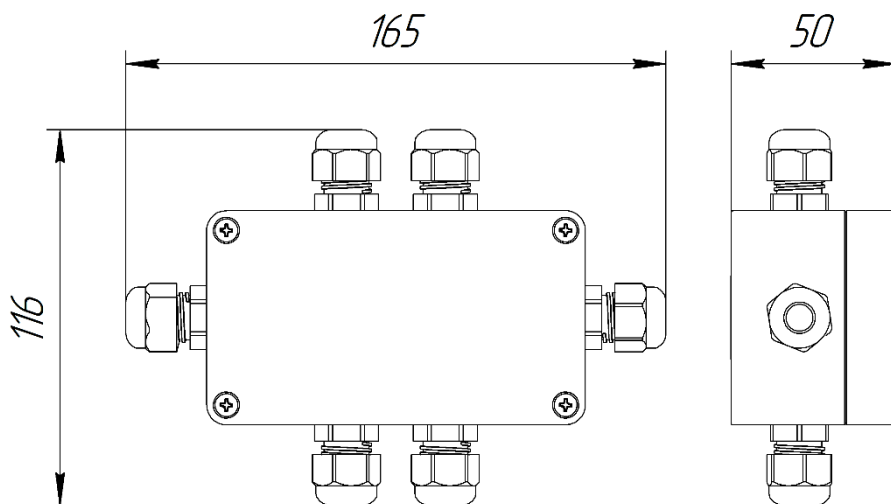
Габаритный чертеж разветвителя RS-SPLIT-6S-IP65
